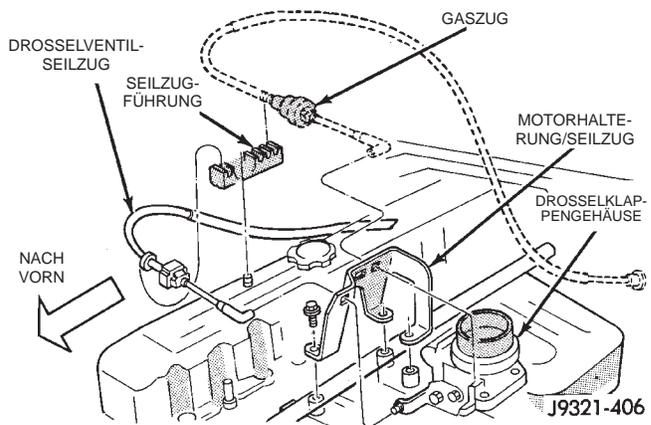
Befestigung des Drosselventil-Seilzugs am Motor
